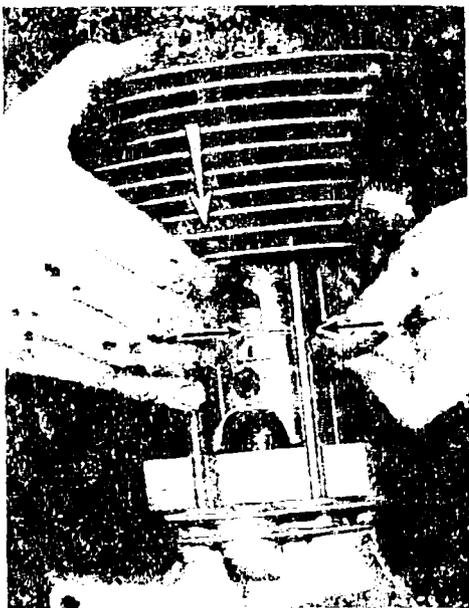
Aufschieben des Zylinders; Kolben auf Holzleiste auflegen, Ringe in Ringnuten eindrücken, so daß Ringenden an den Sicherungstiften liegen
